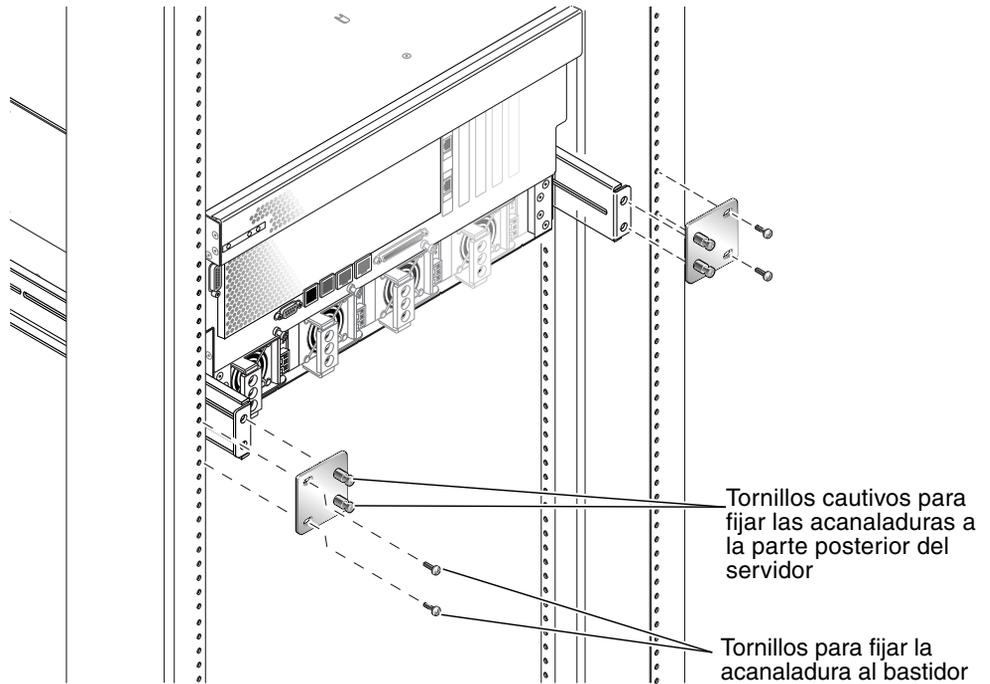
Fijación de la acanaladura de montaje posterior
